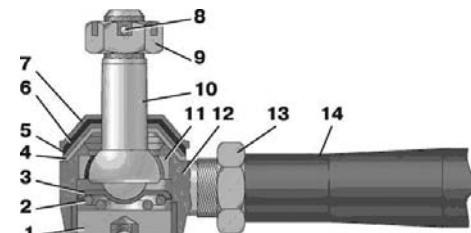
Шарнір рульових тяг: 1 – заглушка; 2 – пружина; 3 – пята; 4 – шайба сферична нижня; 5 – шайба сферична верхня; 6 – захисне кільце; 7 – пружинний ковпак; 8 – шплінт; 9, 13 – гайки; 10 – шаровий палець; 11 – сухар; 12 – наконечник; 14 – тяга
